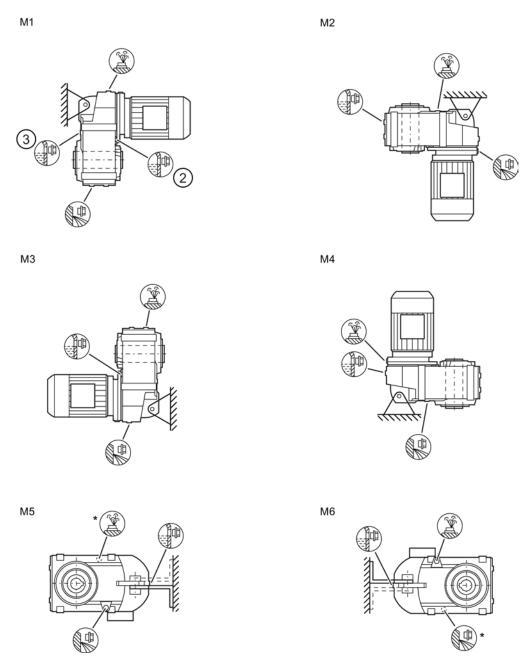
Posiciones de montaje para reductor de ejes paralelos F.AD en versión enchufable, tamaños 39 - 149
